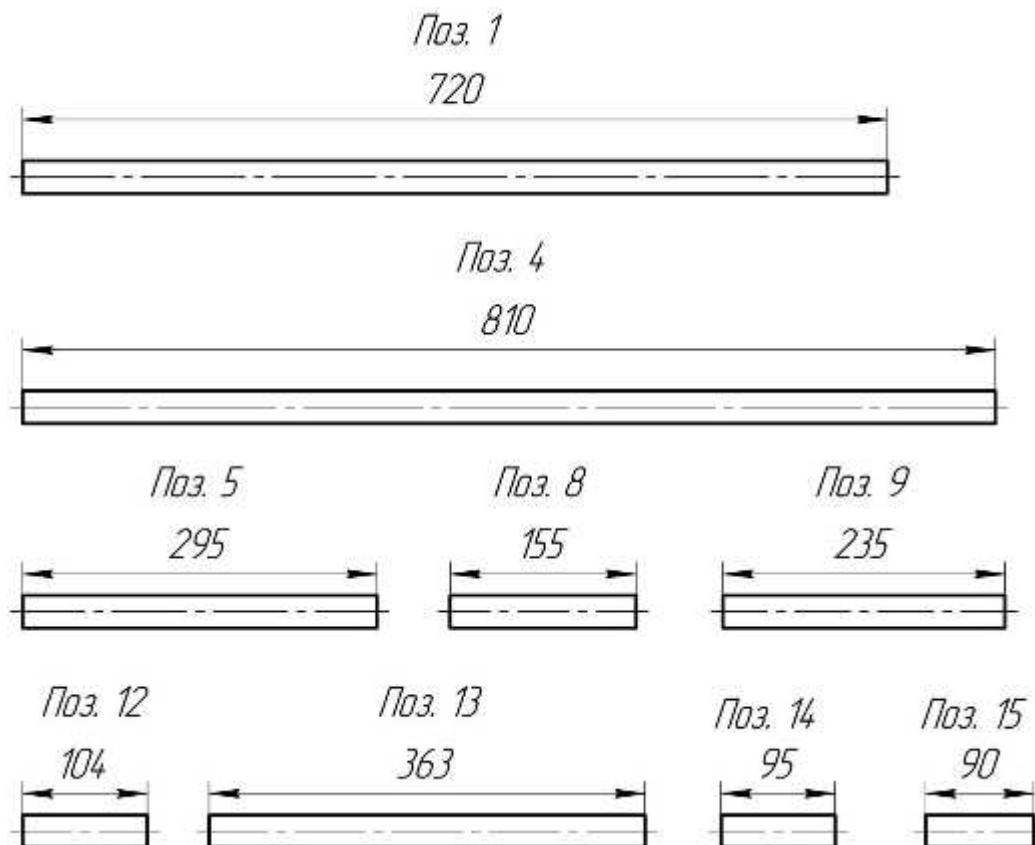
Геометрические размеры заготовок трубок и патрубков
